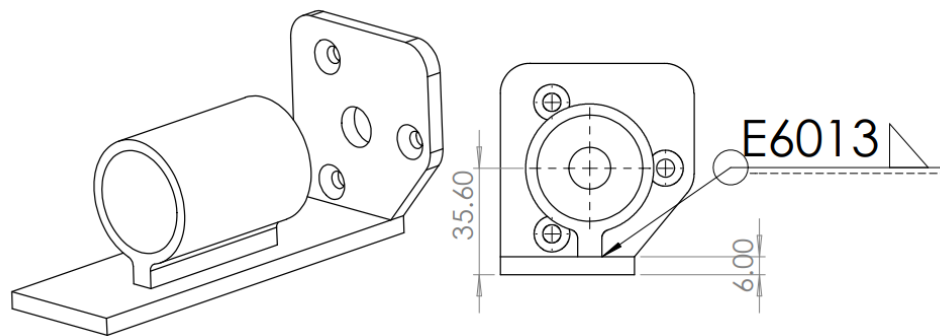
Detalle de soldadura en sistema de elevación. El autor.
